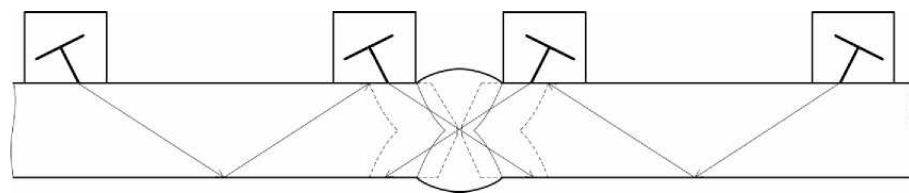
Схема контроля стыковых сварных соединений выполненных двухсторонней сваркой.
